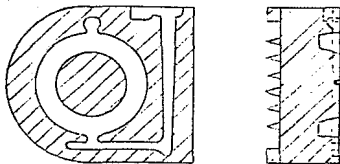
Vista de frente y corte seccional de una de las 2 partes de que consta un molde permanente.
